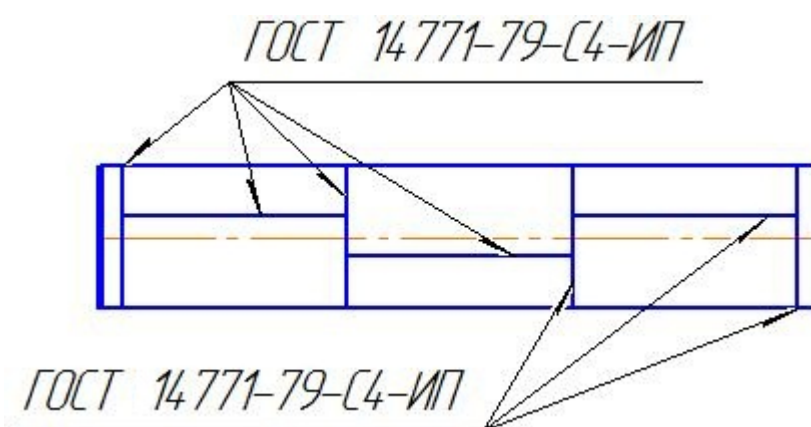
Схема сварных соединений корпуса двигателя метеорологической ракеты МР-20
